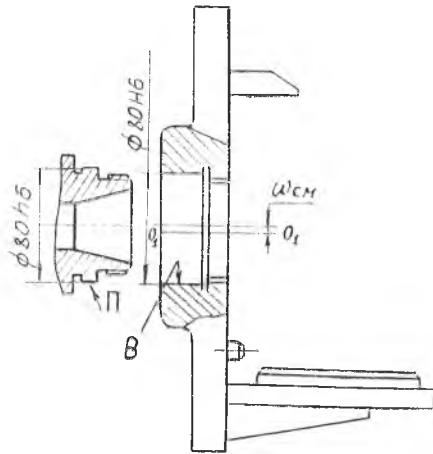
Погрешность установки $\omega_{у.пр}$ при соединении корпуса приспособления со шпинделем
